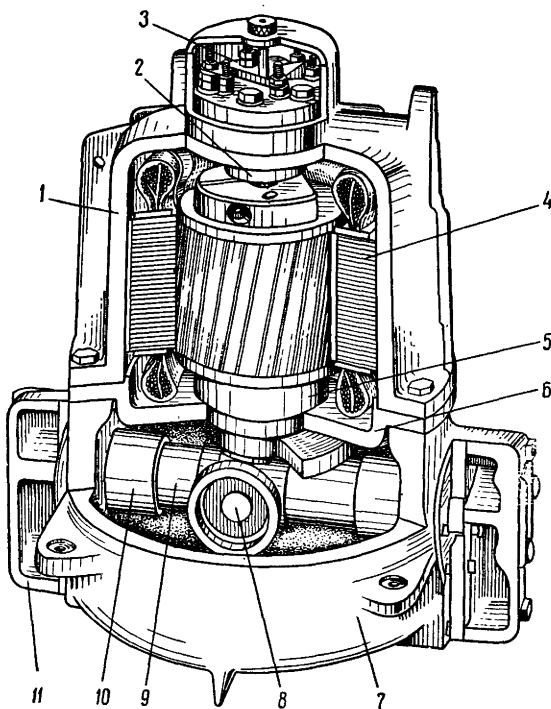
Бесальниковый компрессор с кривошипно-кулисным механизмом.
